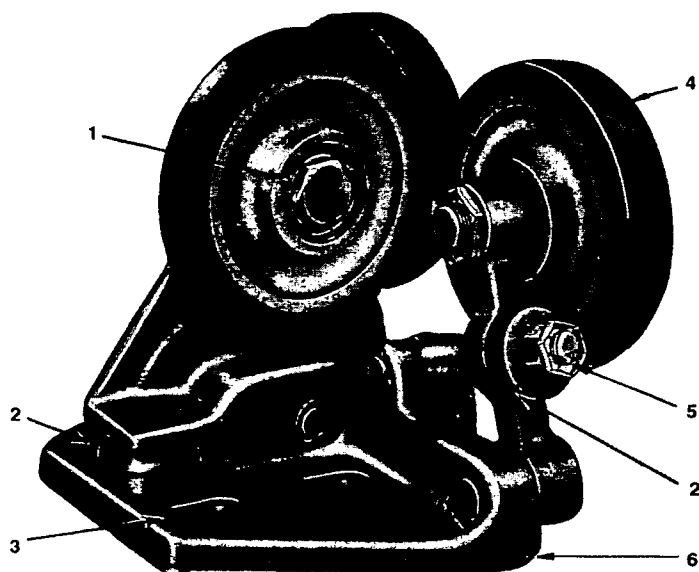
Роликовый башмак с резиновыми прокладками (Moline Accessories Co.): 1 — два крупных прецизионных шарикоподшипника на колесо, 2 — резиновые прокладки, 3 — монтажные пазы для взаимозаменяемости башмаков, 4 — ролики с резиновыми ободами, 5 — болты для центровки и регулирования давления, 6 — литой корпус с механически обработанной опорной частью
